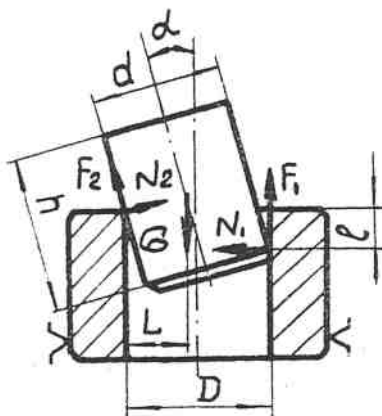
Схема вертикальной сборки вала с втулкой
